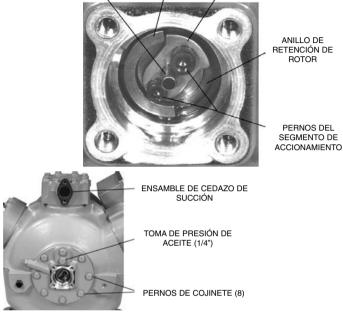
Cómo Retirar la Cabeza de Cojinete del Extremo de Bomba (Compresor 06D)
